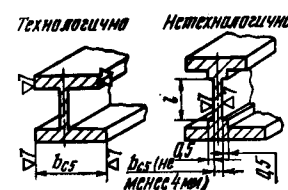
Расположение фиксирующих поверхностей для боковых роликов.
